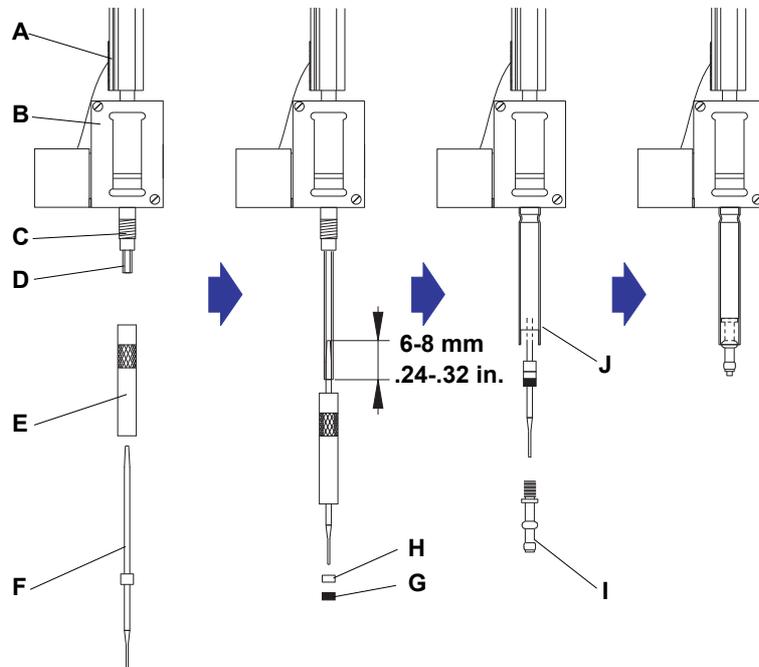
Installation du mécanisme de prélèvement des embouts jetables
